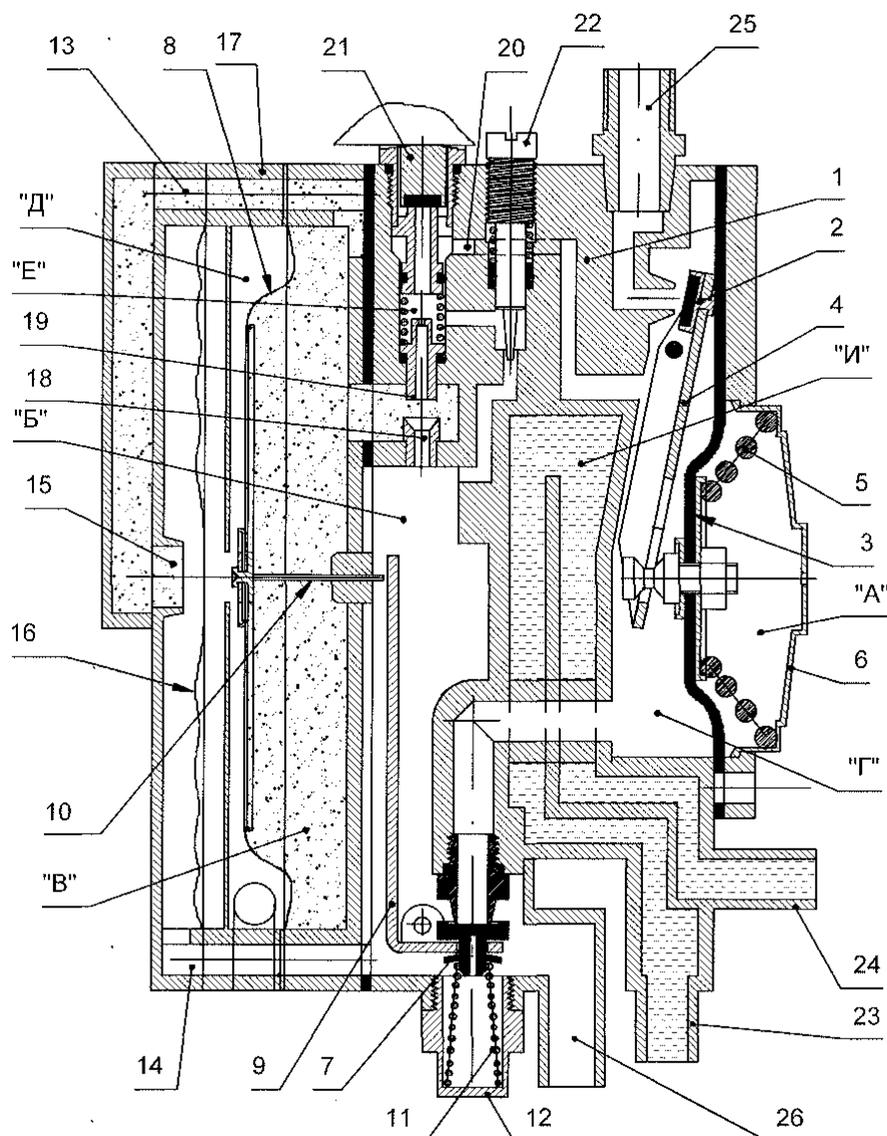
Редуктор – испаритель ГБА -2
